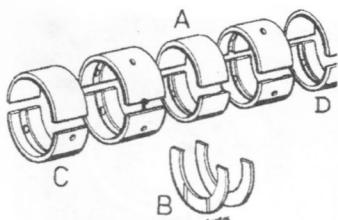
Положение вкладышей коренных подшипников с пазами и без пазов (Раздел 37)
